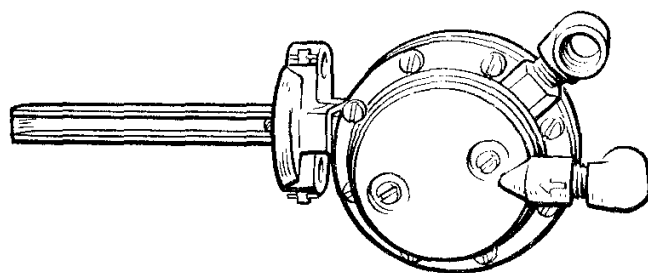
Положение штуцеров головки и крышки относительно корпуса насоса
